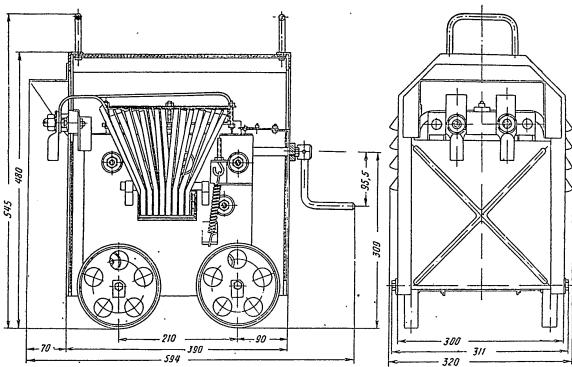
Общий вид и габаритные размеры реактора РТС-500
